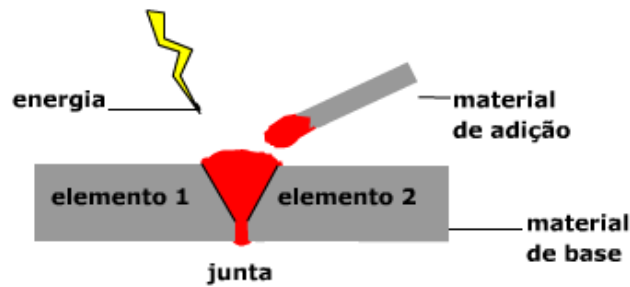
Processo de soldagem por fusão usando material de adição.
